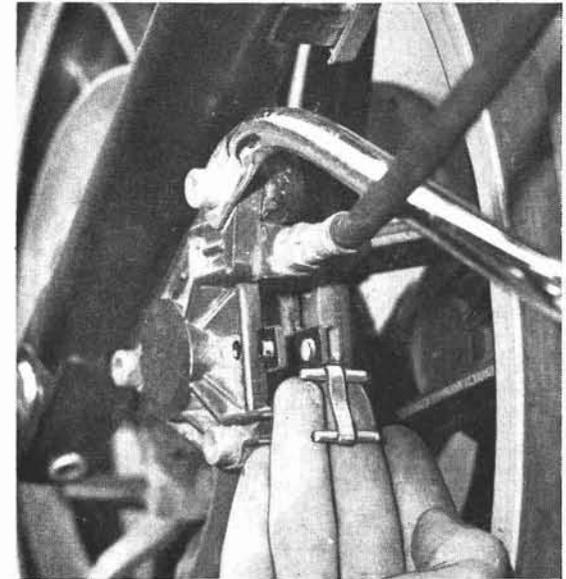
Ressort et goupilles d'appui (Photo RMT)
